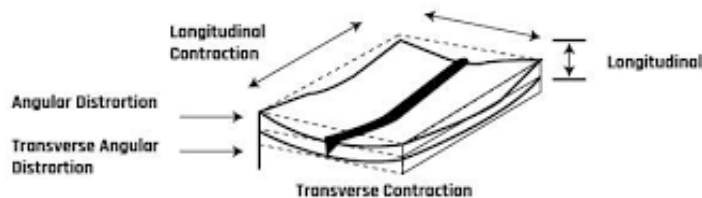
Deformação *buckling* após soldadura [4].
